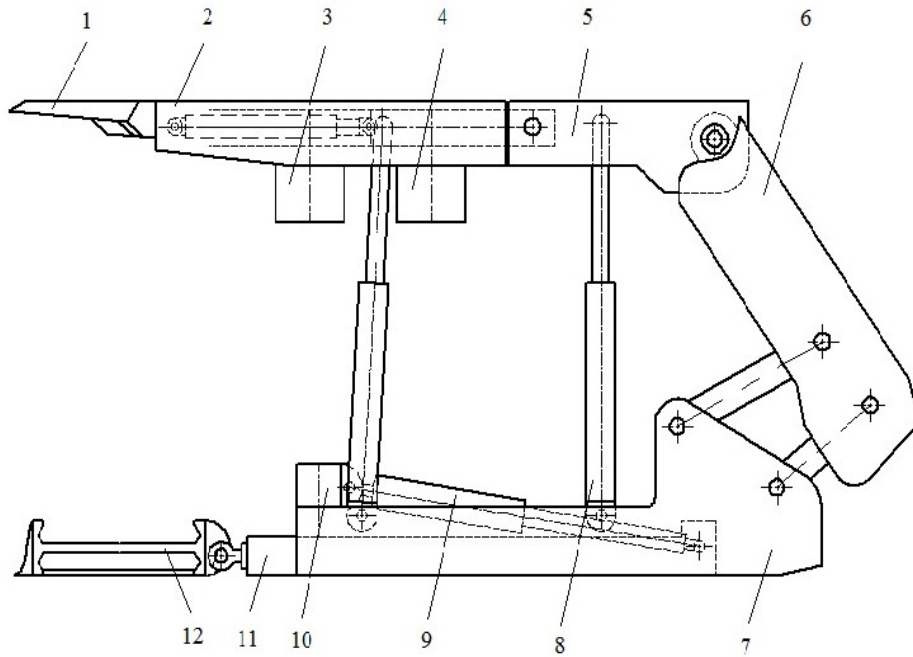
Секция гидрофицированной крепи с телескопическим перекрытием
